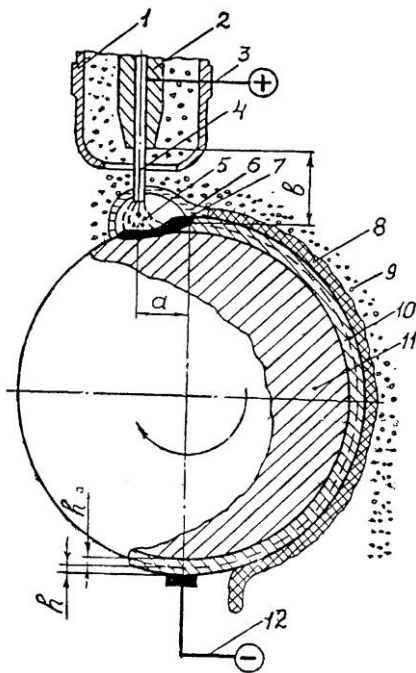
Схема процесса автоматической наплавки цилиндрической детали под слоем флюса:
